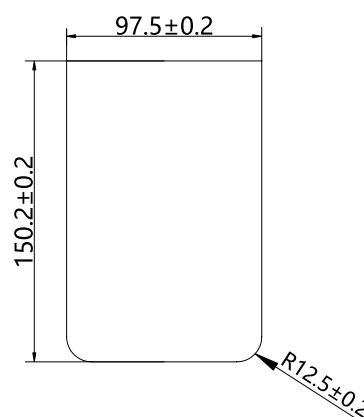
Чертеж установки опорной пластины (вырез в двери шкафа)
